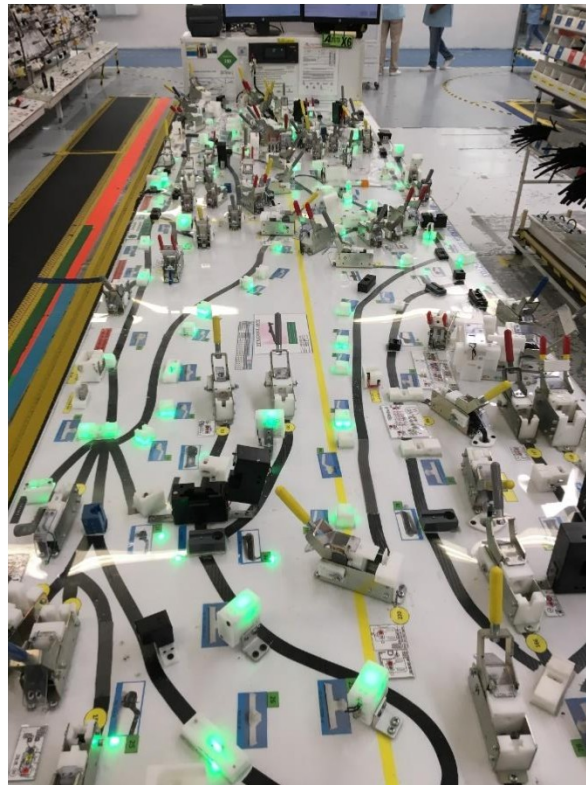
Tablero de prueba eléctrica actual, liberado y colocado en línea de producción, con número de parte "Z" cargado, vista superior derecha. Foto por Eduardo Trujillo.
